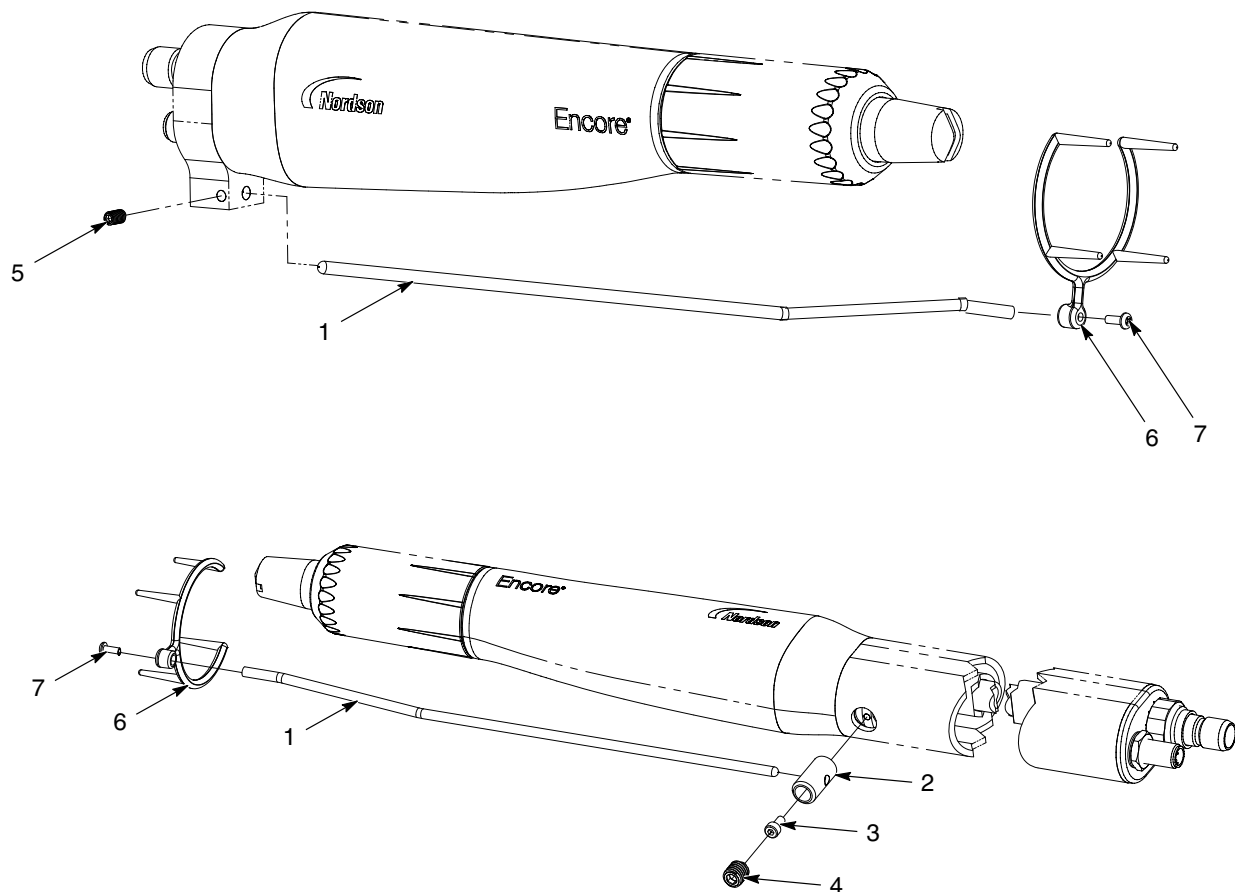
Pistolholdestang til pistoler til montering på holdestang
